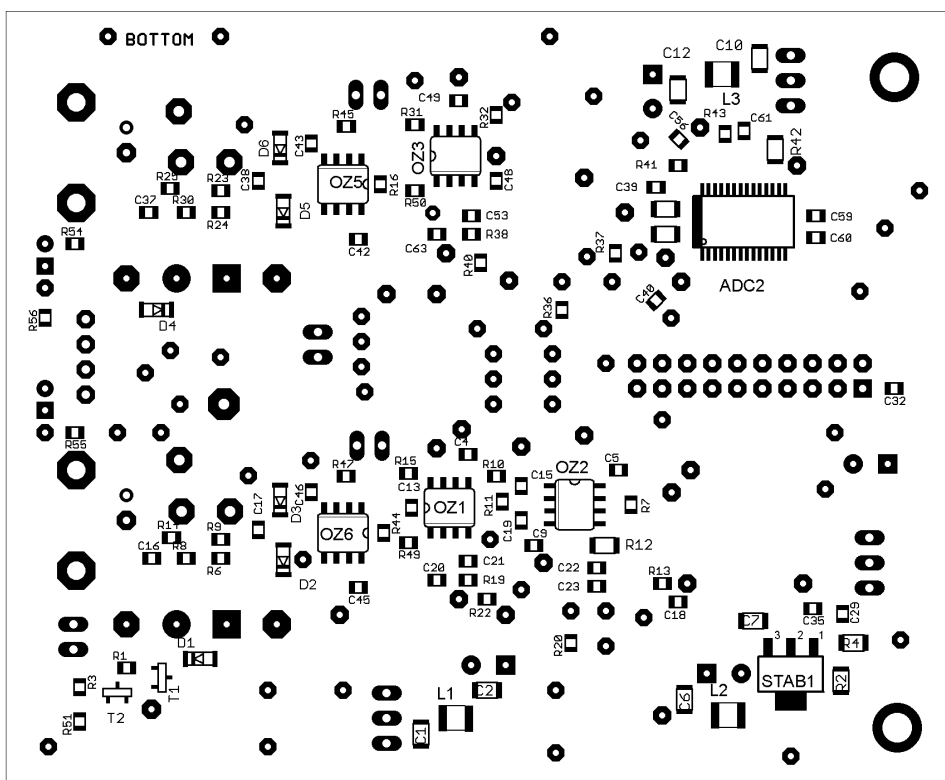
PCB zdroja: modulu lineárnych stabilizátorov 68,3 x 67,3 mm
